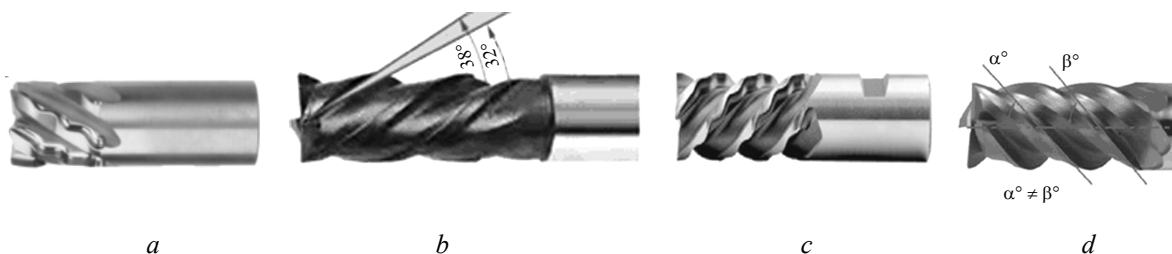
Конструкции концевых фрез для обработки деталей сложного профиля из титана различных фирм: a – ООО «ПК МИОН» (Россия); b – Weldon (США); c – STOCK (Германия); d – Mitsubishi (Япония)
